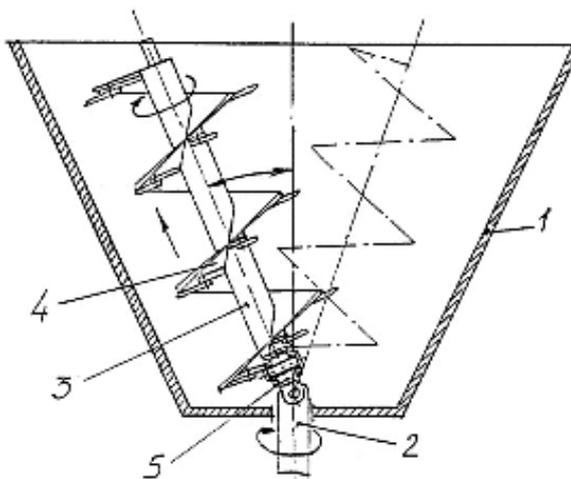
Способ приготовления кормосмеси в бункерном смесителе и смеситель кормов (патент №2311753)
